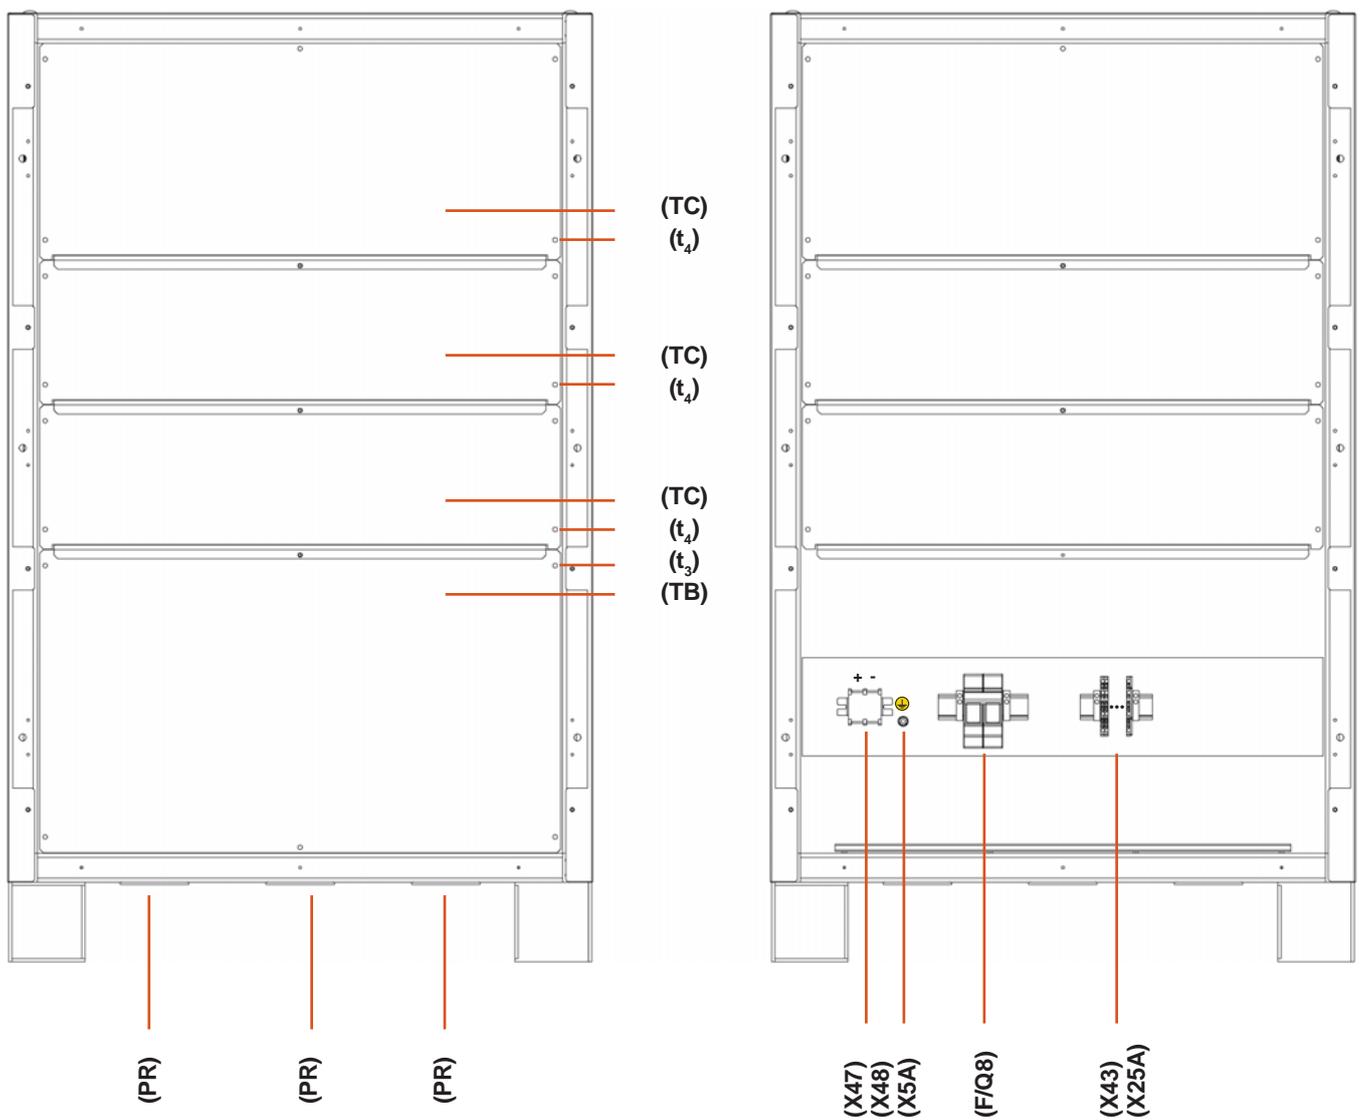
Vue frontale armoire de batteries de 605x805x1315 mm.
